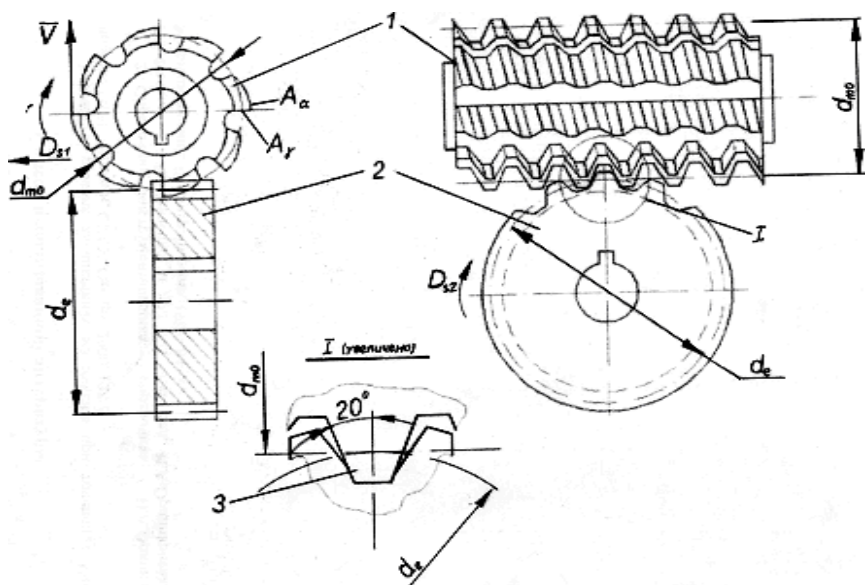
Схема нарезания зубчатого колеса червячной модульной фрезой:
